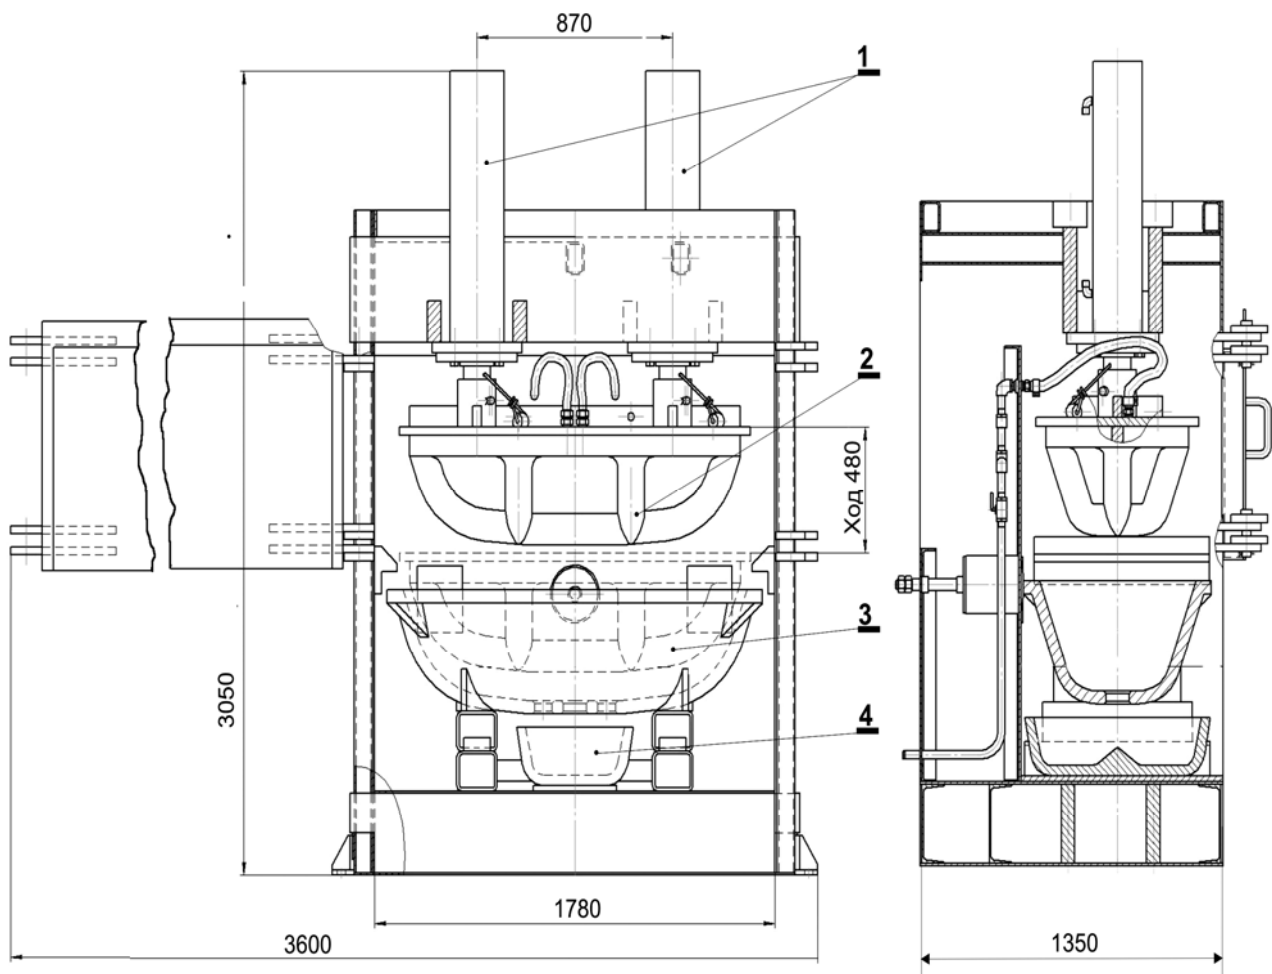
Установка для извлечения металла из алюминиевого шлака: 1 – гидроцилиндр; 2 – пуансон; 3 – шлаковница; 4 – изложница
